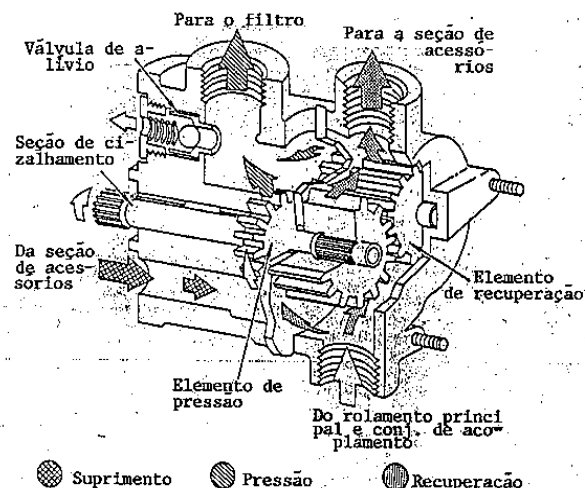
Vista em corte de uma bomba de engrenagem.
